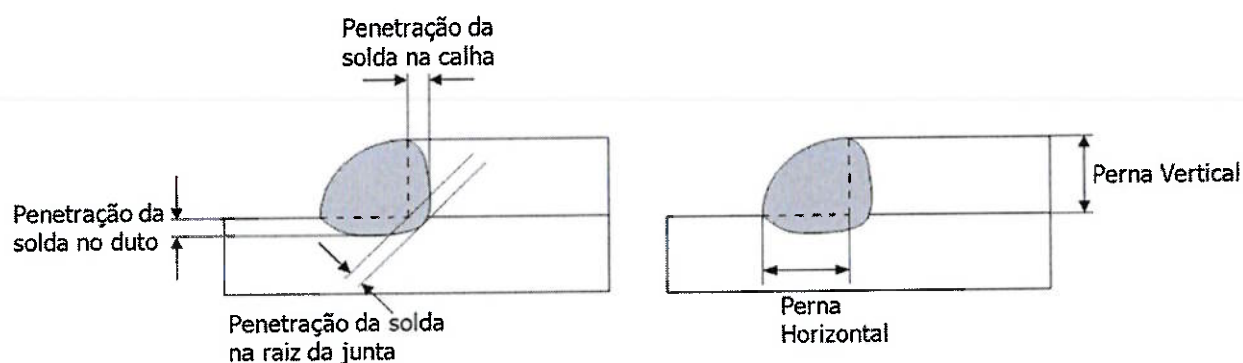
Dimensional da solda para os ensaios de macrografia.
